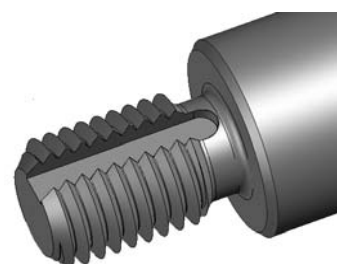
Паз на резьбовом конце вала под многолапчатую стопорную шайбу
